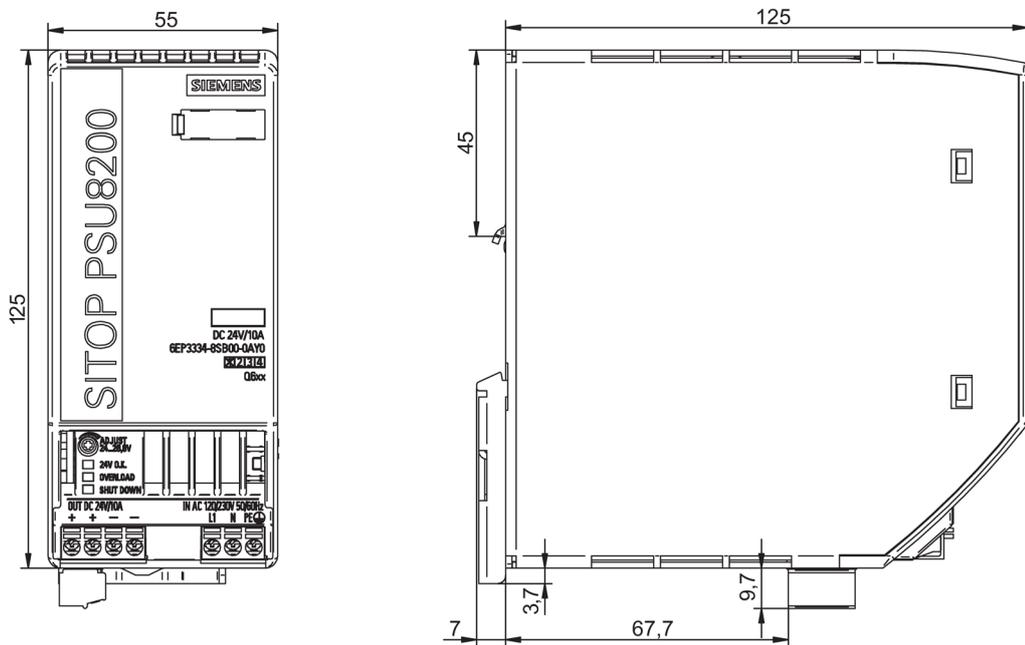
Maßzeichnung 6EP3334-8SB00-0AY0
